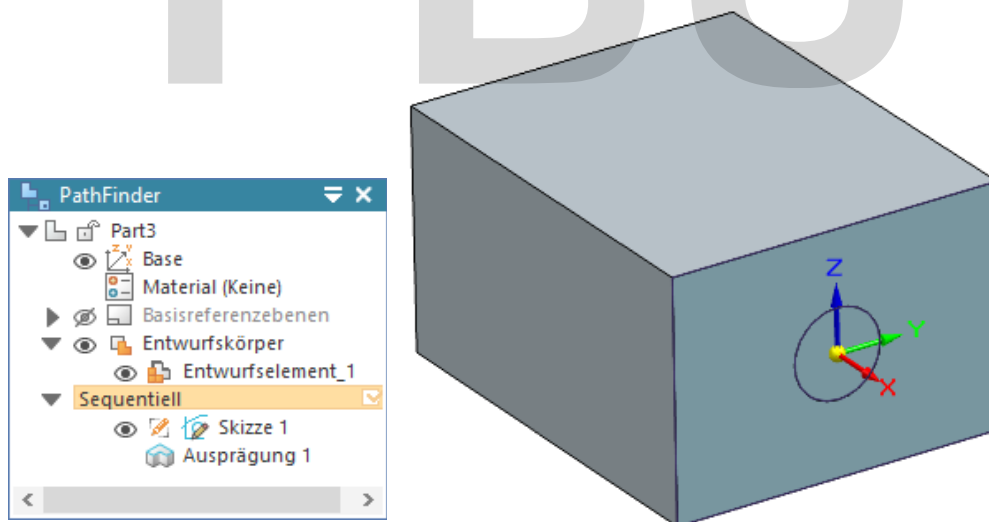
Die Extrusion auf Basis der Skizze
